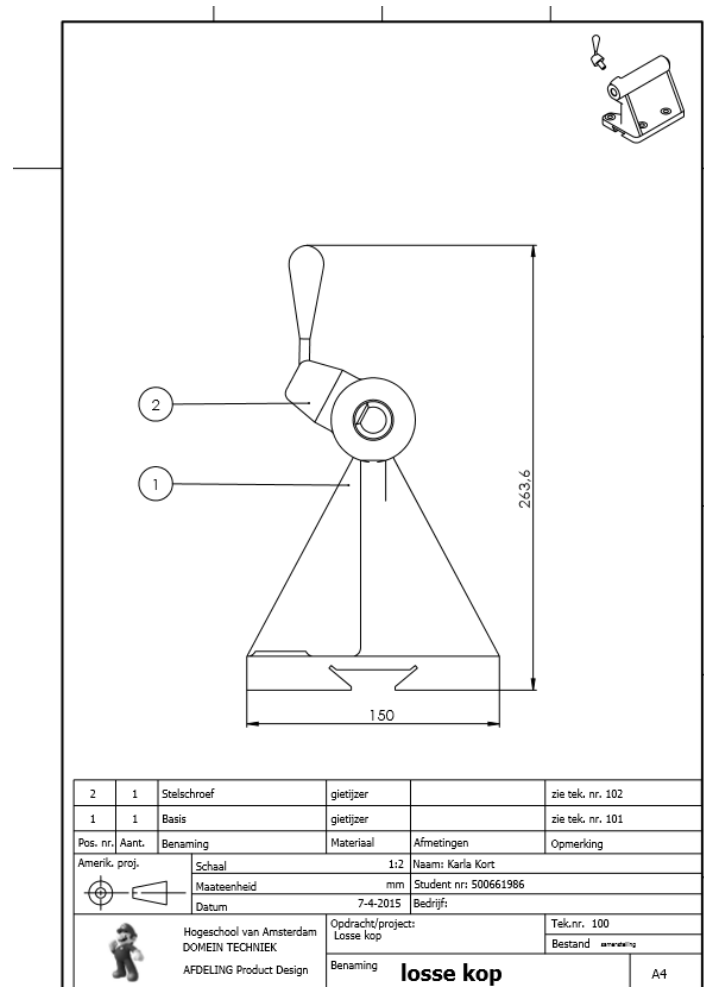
Exemplo de um desenho técnico [Kort 2017].
